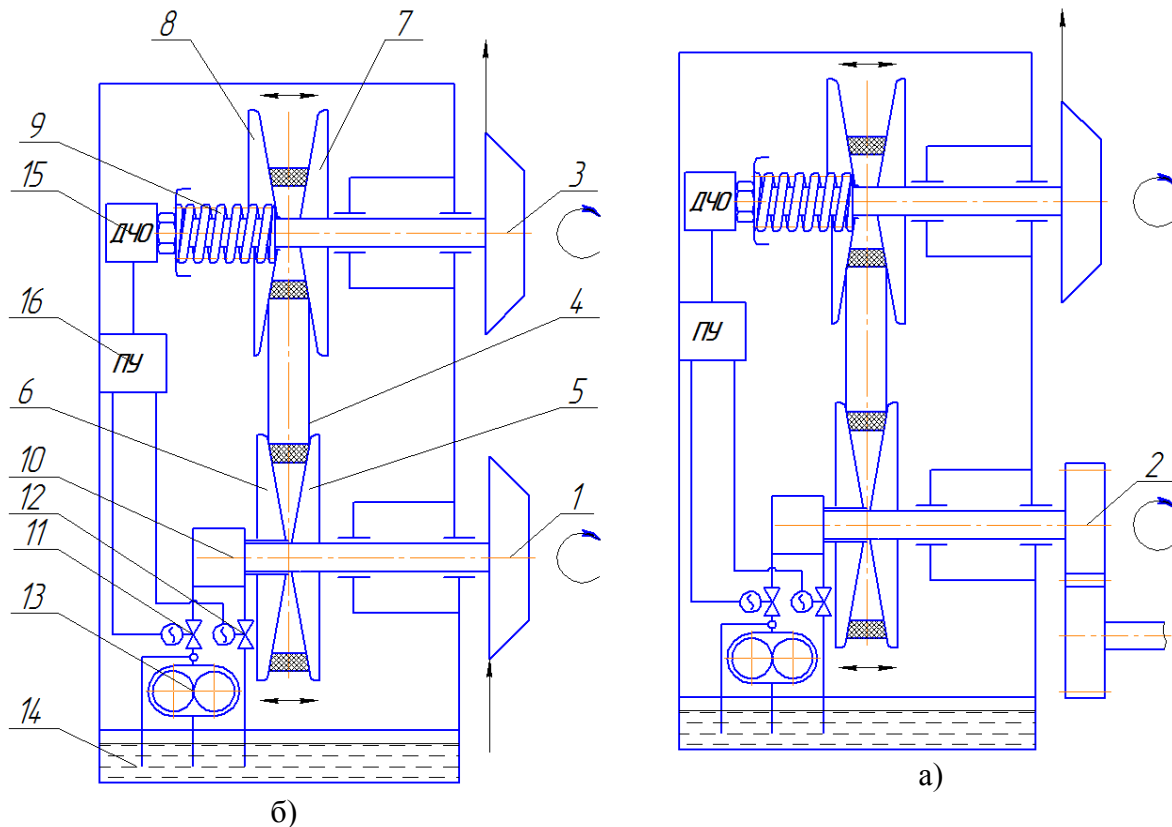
Турбокомпресор з газовою турбіною (а) та механічним приводом (б): 1 - газова турбіна; 2 - механічний привід; 3 - відцентровий компресор; 4 - ремінна передача; 5 - ведучий шків; 6, 8 - рухомий диск; 7 - ведений шків; 9 - пружина стискання; 10 - обертовий гідроциліндр; 11, 12 - електромагнітний клапан; 13 - масляний насос; 14 - масляна ванна; 15 - датчик частоти обертання; 16 - пульт управління
